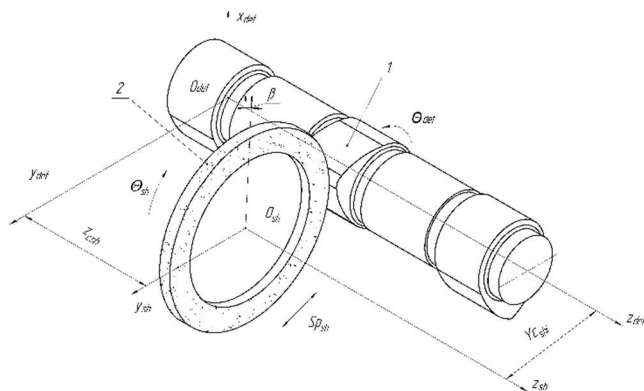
Схема обробки розподільчого вала фірмою Junker
